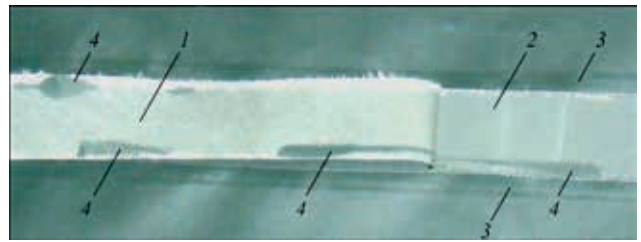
Зварний шов ламінованої тканини Unisol 950 з локальними непроварами по шву після випробування на відрив з'єднувальної стрічки: 1 – відірвана стрічка з оголеним кордом; 2 – зварний шов; 3 – зона термічного впливу біля шва; 4 – ділянки непровару на стрічці та на шві
